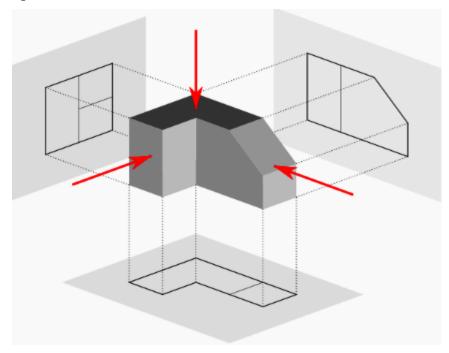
Projection orthogonale d'un objet sur 3 plans de projection (27)
